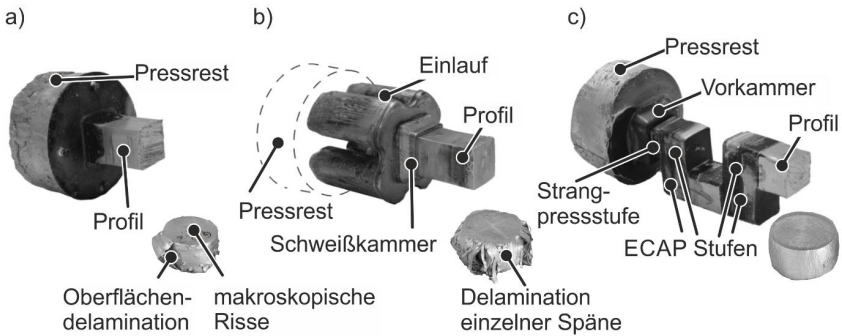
Werkstofffluss und Stauchproben für unterschiedliche Werkzeugdesigns ($R = 8,6$): a) Flachwerkzeug, b) Kammerwerkzeug, c) iECAP-Werkzeug (Misiolek et al., 2012)
